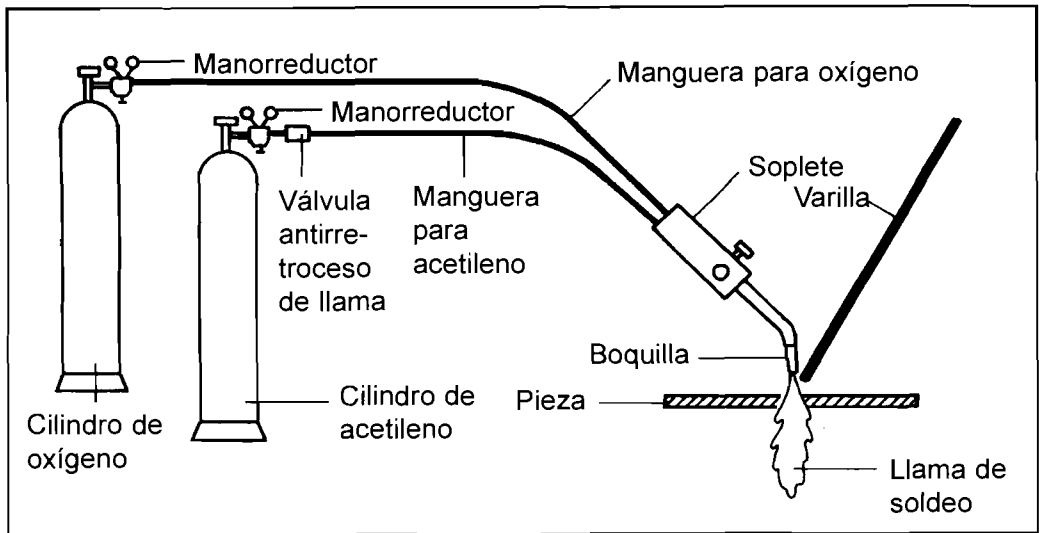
EQUIPO DE SOLDEO OXIACETILÉNICO
